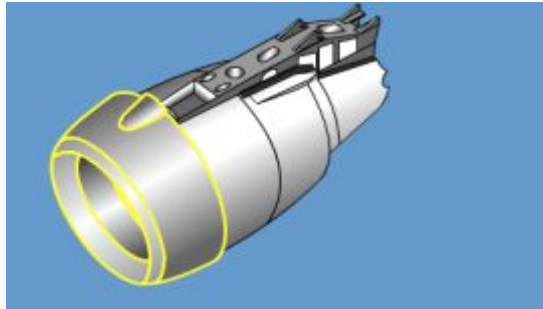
Conjunto de nacelas pertenecientes al motor.
